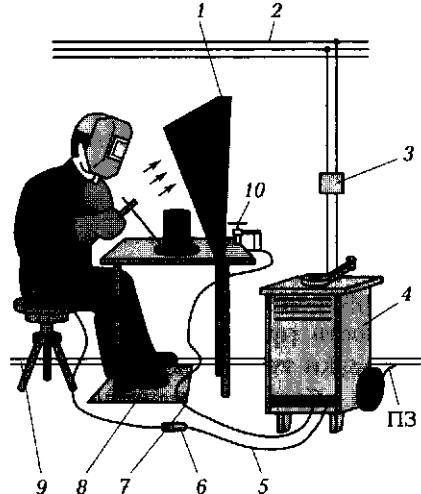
Сварочный пост ручной дуговой сварки:
